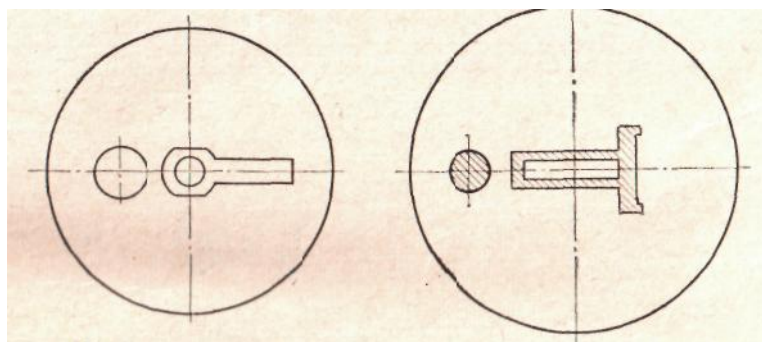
Матриця для пресування порожнього профілю несиметричного перерізу з паразитним отвором
